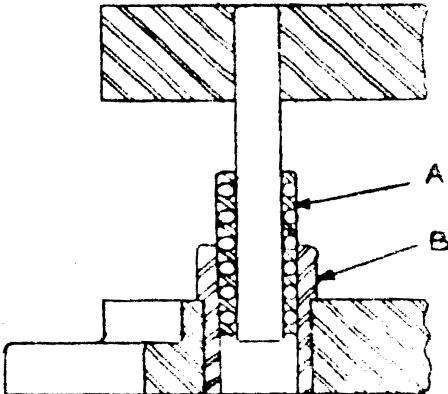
Montaje en que se utiliza cojinetes de bolas en lugar de casquillos guía.
